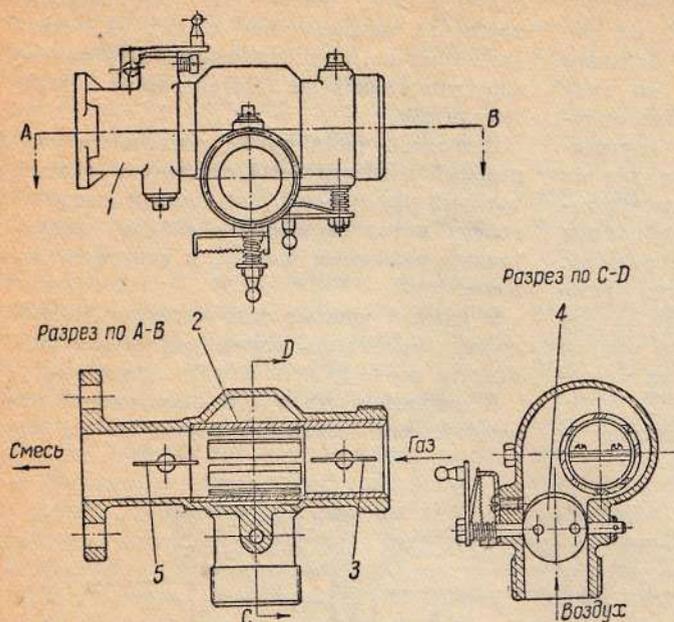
Газогенераторная установка. Газосмеситель к бензиновому двигателю В-3. Общий вид
